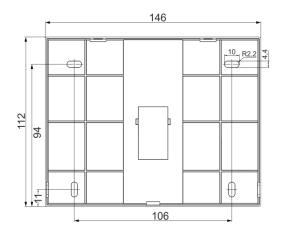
Установочный чертеж основания корпуса ВПУ-А24/700(О)
